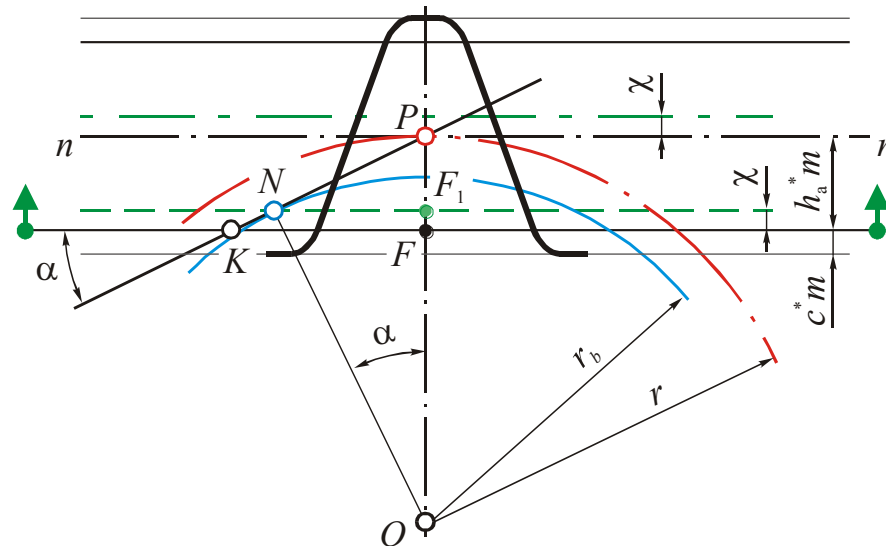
Схема зачеплення інструментальної рейки і заготовки, коли має місце підрізання ніжок зубців
